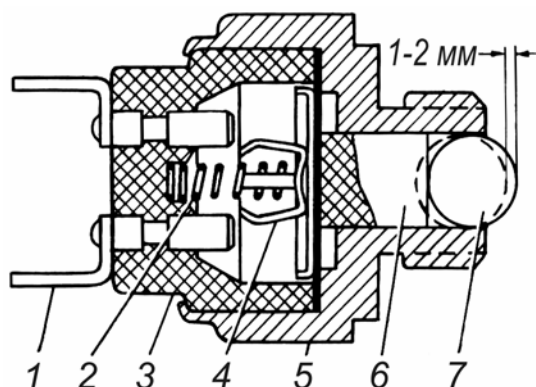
Выключатель света заднего хода: 1 - вывод; 2 - пружина; 3 - изолятор; 4 - контактная пластина; 5 - корпус; 6 - толкатель; 7 - шарик
